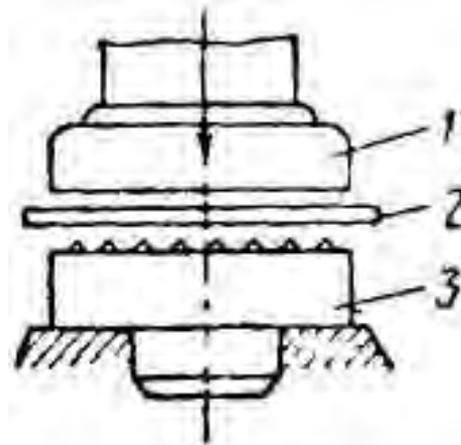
Схема рельефной штамповки при изготовлении шкал
